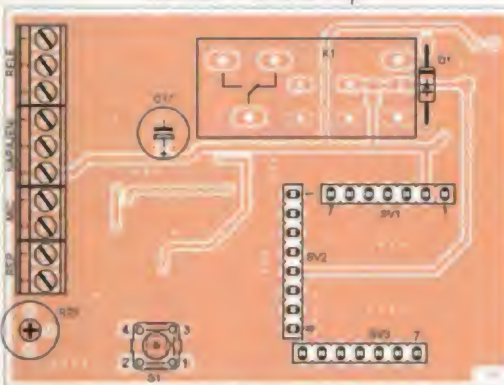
Univerzální deska s plošnými spoji modulů - strana Bottom
